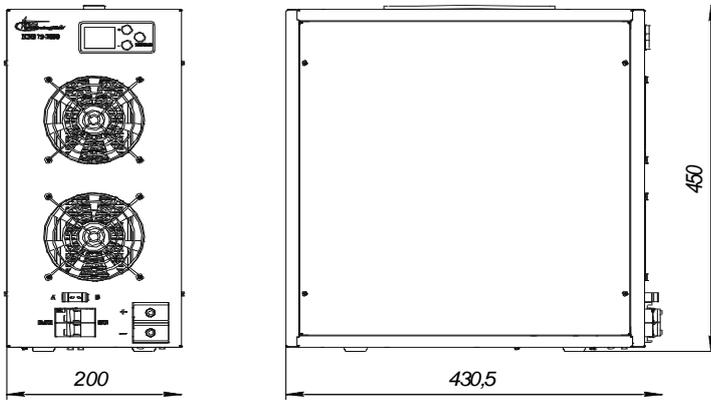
Габаритный чертеж НЭВ 75-2000
